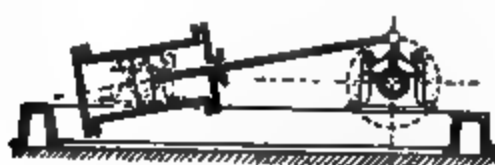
Oscillierende Maschine. Cylinder wird leicht unrund.
